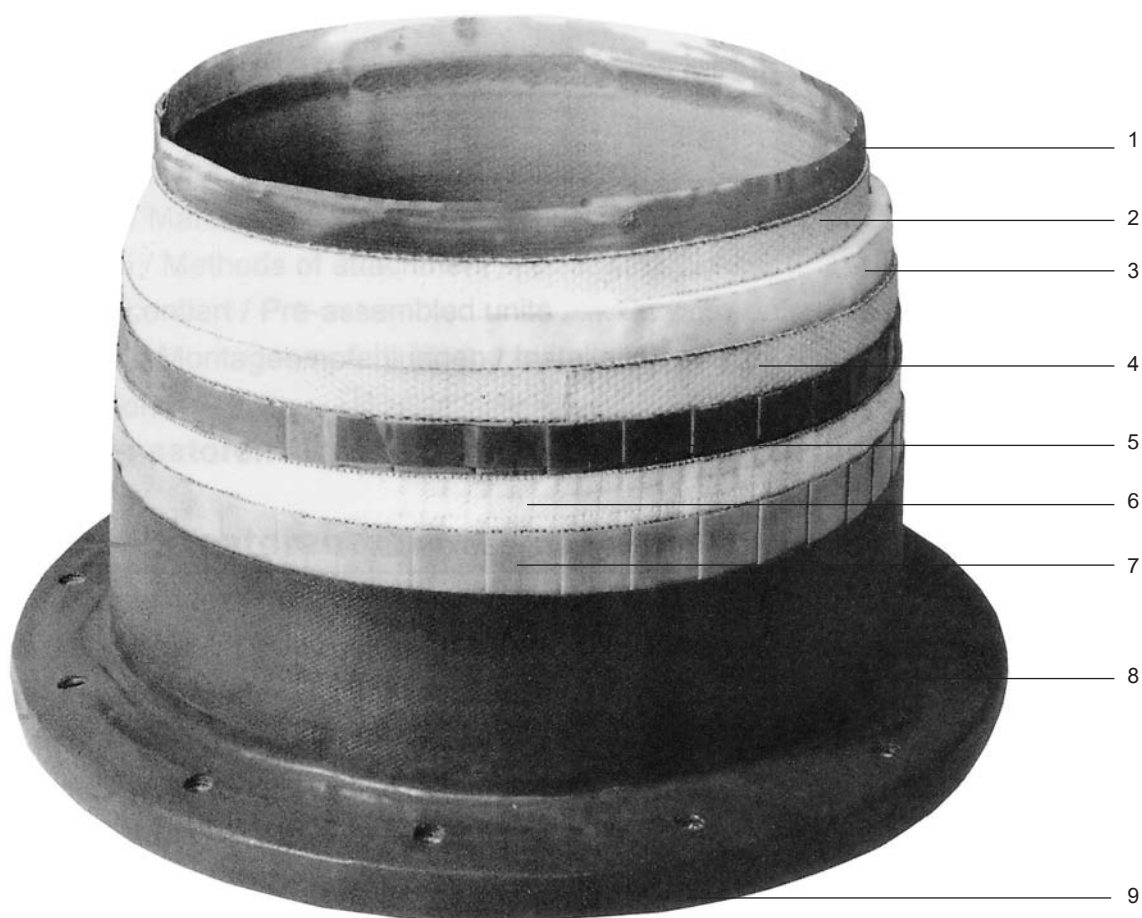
typ 33 s jednou vlnou a vnitřním výztužným kruhem
